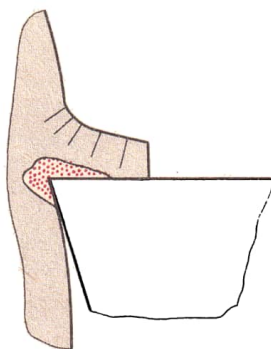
Schneidenaufbau drückt sich ins Werkstück ein
